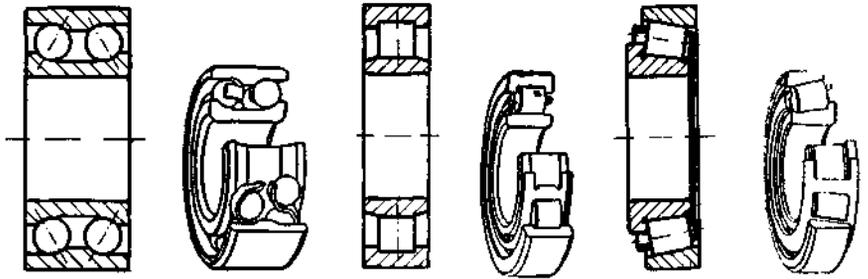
Cojinete de doble hilera de bolas.* *Figura 16.* — *Cojinete de rodillos cilindricos.* *Figura 17.* — *Cojinete de rodillos cónicos.
